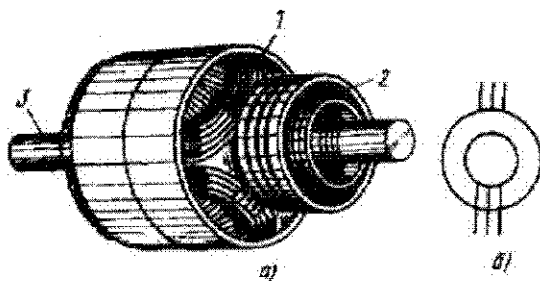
Внешний вид ротора (а) и условное графическое обозначение (б) асинхронного двигателя с контактными кольцами: 1 - обмотка; 2 - контактные кольца; 3 - вал
